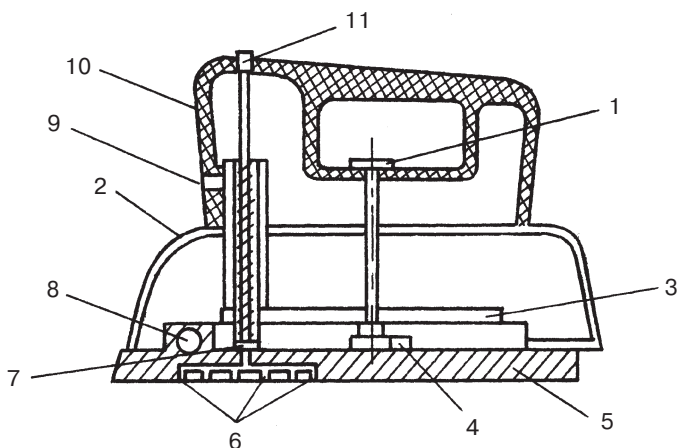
Устройство утюга с терморегулятором и пароувлажителем: 1 — лимб терморегулятора; 2 — корпус; 3 — бак; 4 — биметаллический терморегулятор; 5 — подошва; 6 — каналы; 7 — клапан; 8 — тэн; 9 — отверстие для залива воды; 10 — ручка; 11 — кнопка отпаривателя
